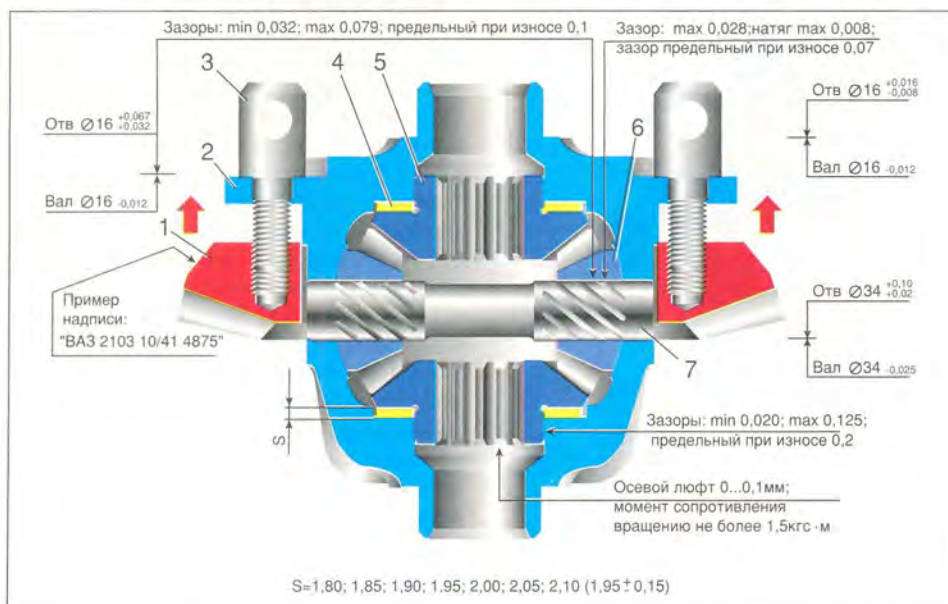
Дифференциал автомобиля "Жигули": 1 – ведомая шестерня дифференциала; 2 – коробка дифференциала; 3 – монтажный болт ведомой шестерни; 4 – опорная шайба; 5 – полуосевая шестерня; 6 – сателлит; 7 – ось сателлитов.
